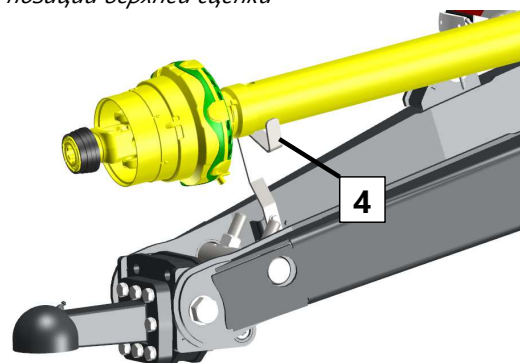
Держатель карданного вала в позиции нижней сцепки
